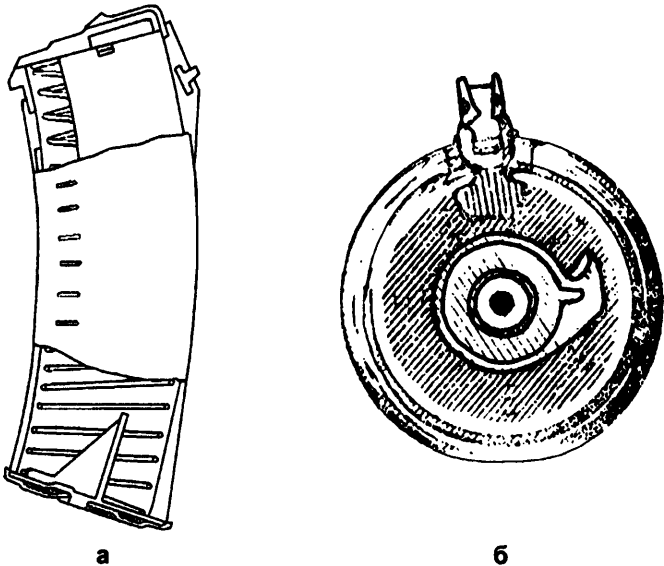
Магазины: а – коробчатого типа; б – барабанного типа
